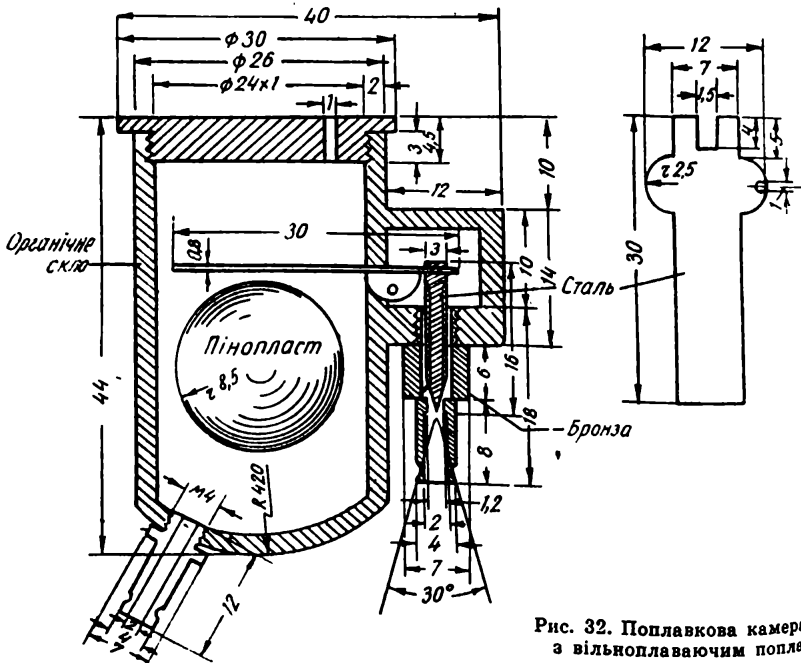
Поплавкова камера з вільноплаваючим поплавком.
